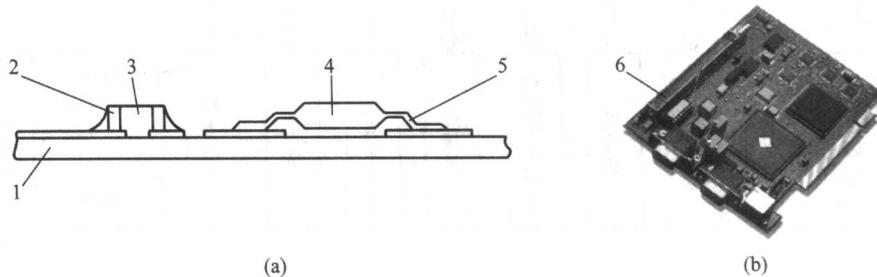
单面组装 SMC/SMD 的 SMA 示意图
